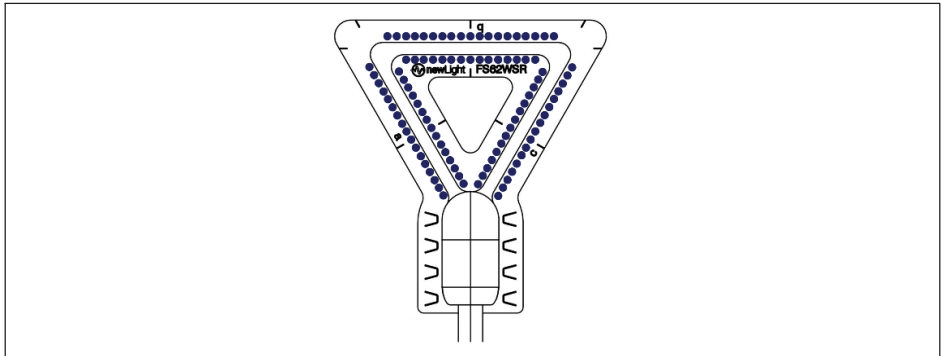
FS62WSR - parcours de soudage 2
